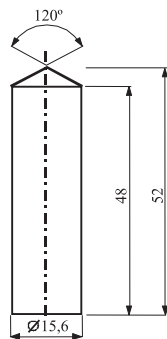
Цилиндрический бронзовый поршень; размеры в мм
